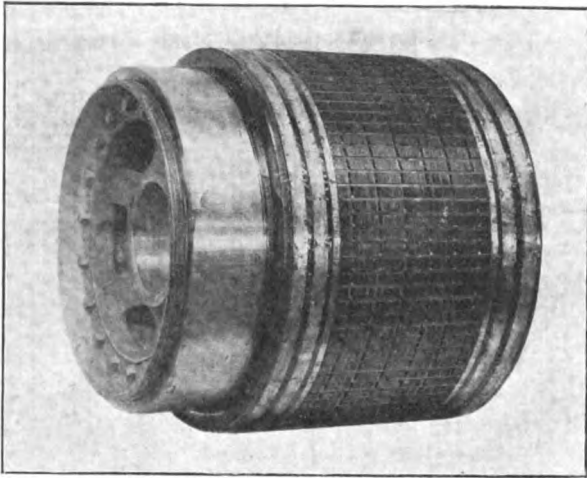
Induit d'un moteur Westinghouse de 250 chevaux.
